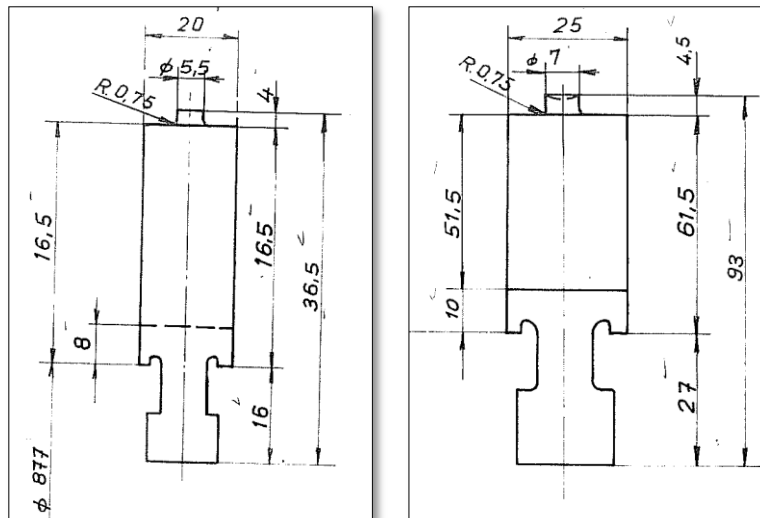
dimensioni principali delle pale del 1° e 6° stadio della macchina n° 2, in ordine partendo da sinistra.
